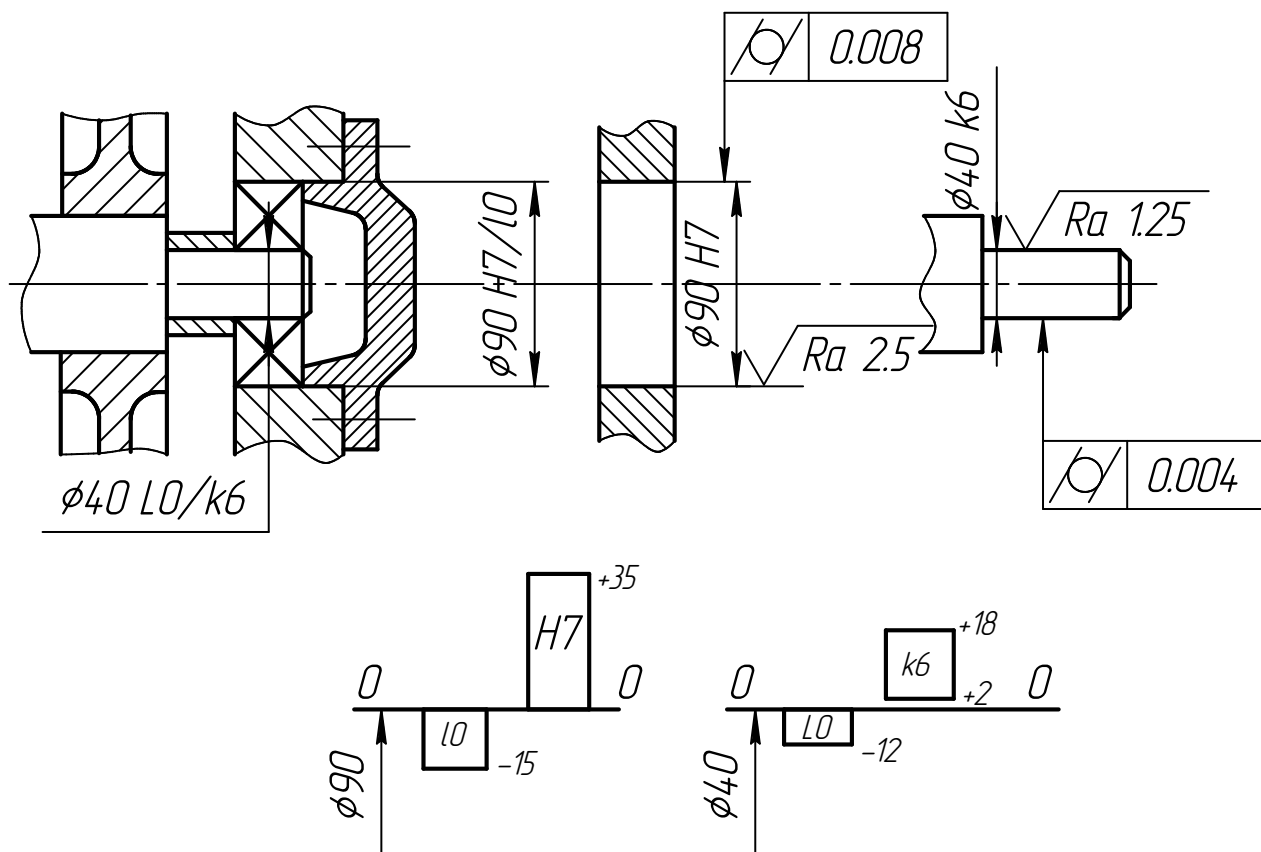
Обозначение посадок подшипников качения на сборочных чертежах
